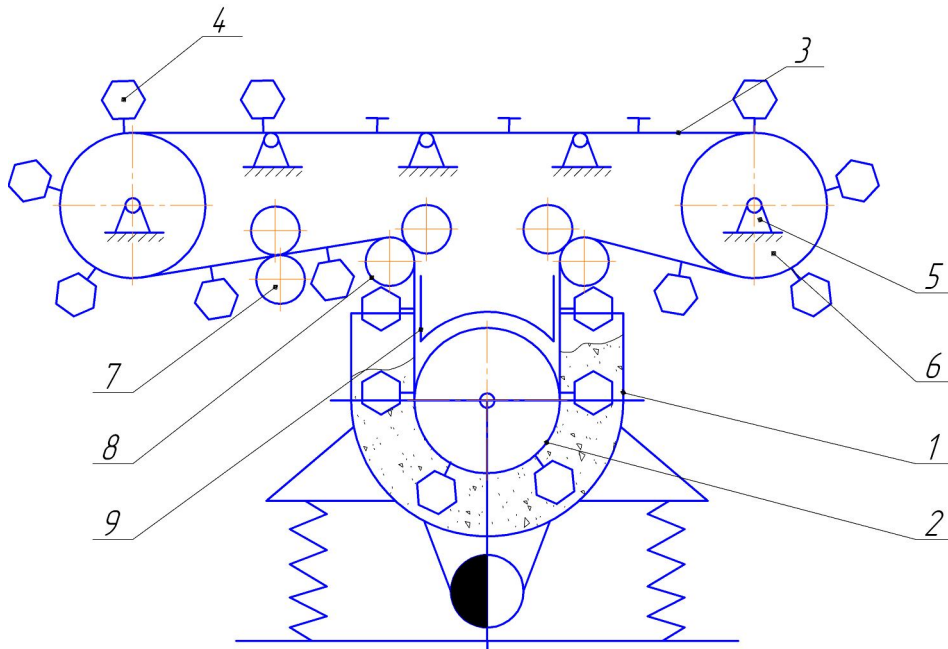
Принципова схема конвеєрної вібраційної машини з транспортером для переміщення закріплених деталей: 1 – робочий контейнер; 2 – приводний барабан; 3 – транспортна стрічка; 4 – деталь; 5 – кріплення деталей; 6 – опорний коток; 7 – тяговий ролик; 8 – гальмівний ролик; 9 – вкладиш з перфорованими стінками
